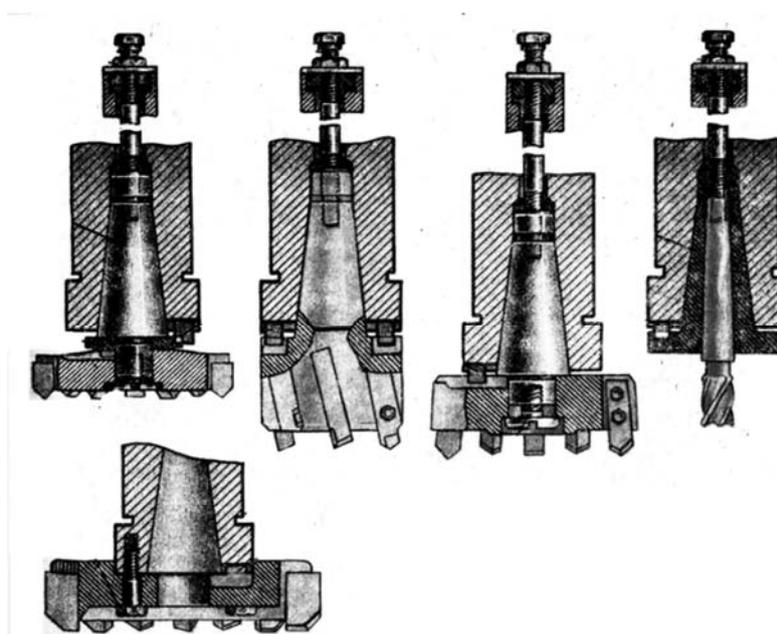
Установка и закрепление торцовых и концевых фрез
